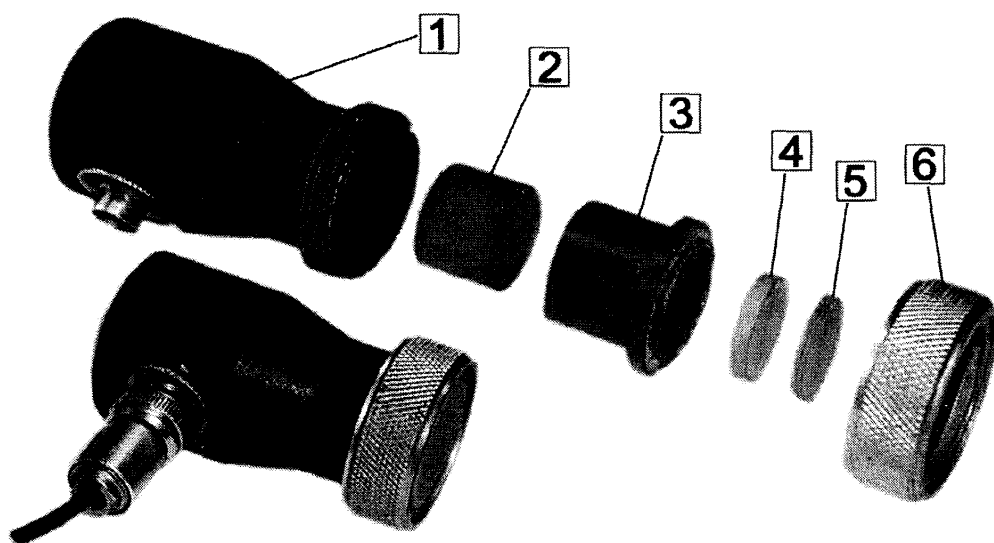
Конструкція багат шарового безконтактного ультразвукового перетворювача:
